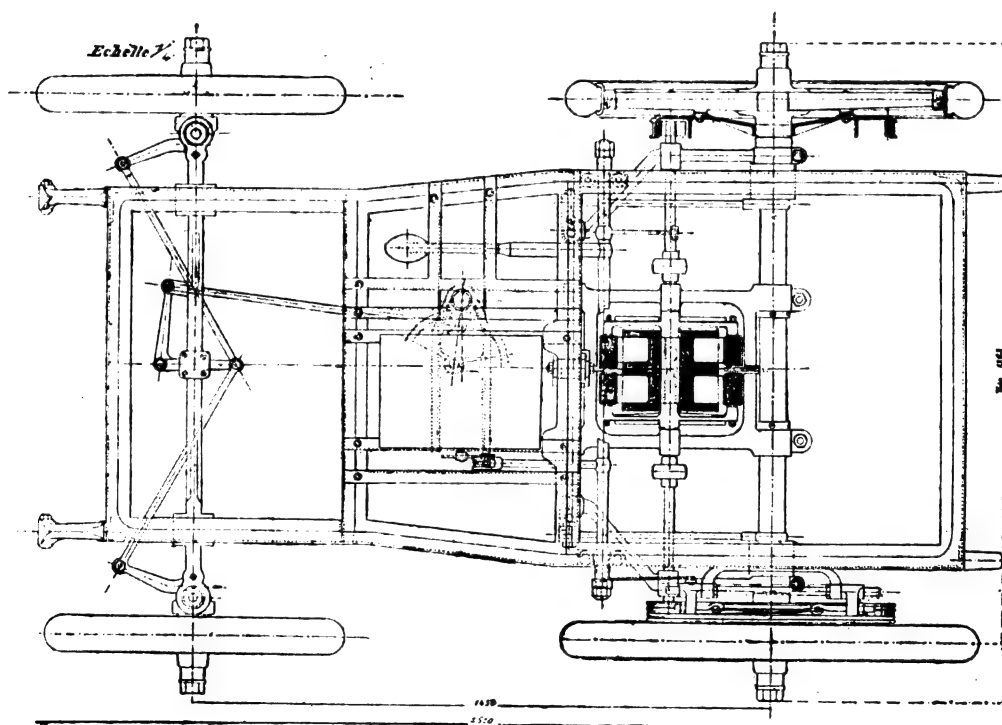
Vue en plan de la voiture Meynier et Legros.
